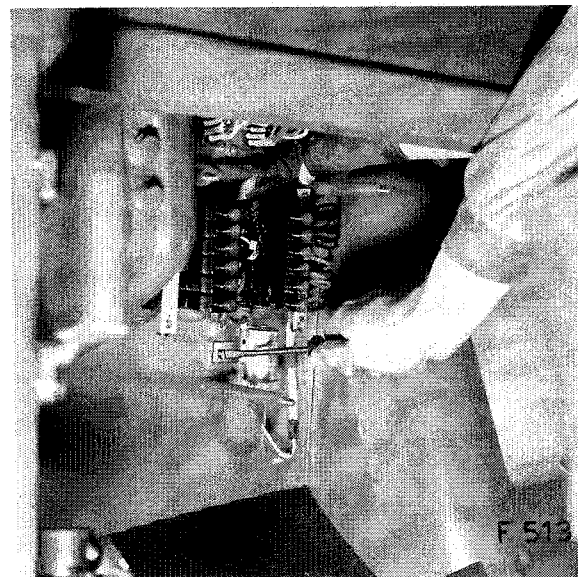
Lösen der Befestigungsschrauben des Blinkgebers
